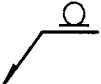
Обозначение одинаковых сварных швов:
